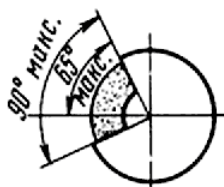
Углы раскрытия кожуха шлифовального круга
